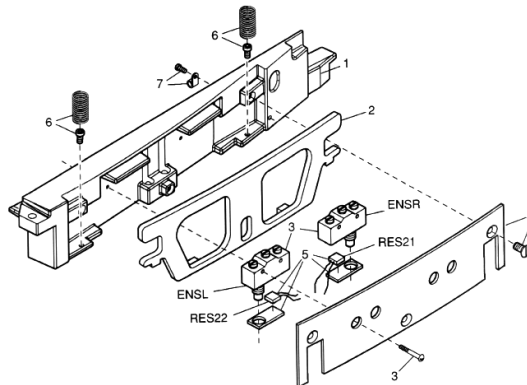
BARRA DE ENTRADA Y SWITCHES
